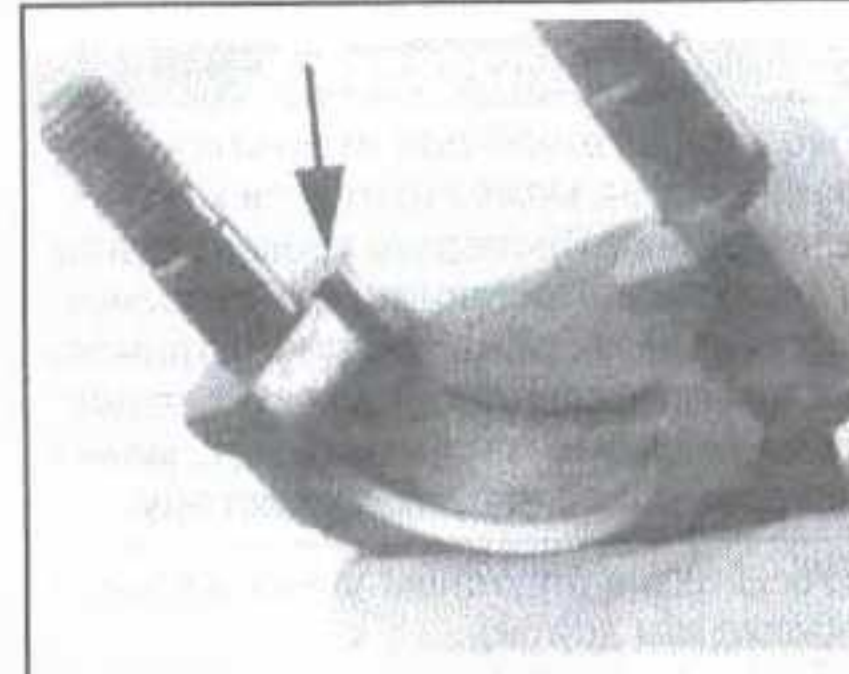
Выемка в крышке подшипника совмещается с выступом во вкладыше подшипника
